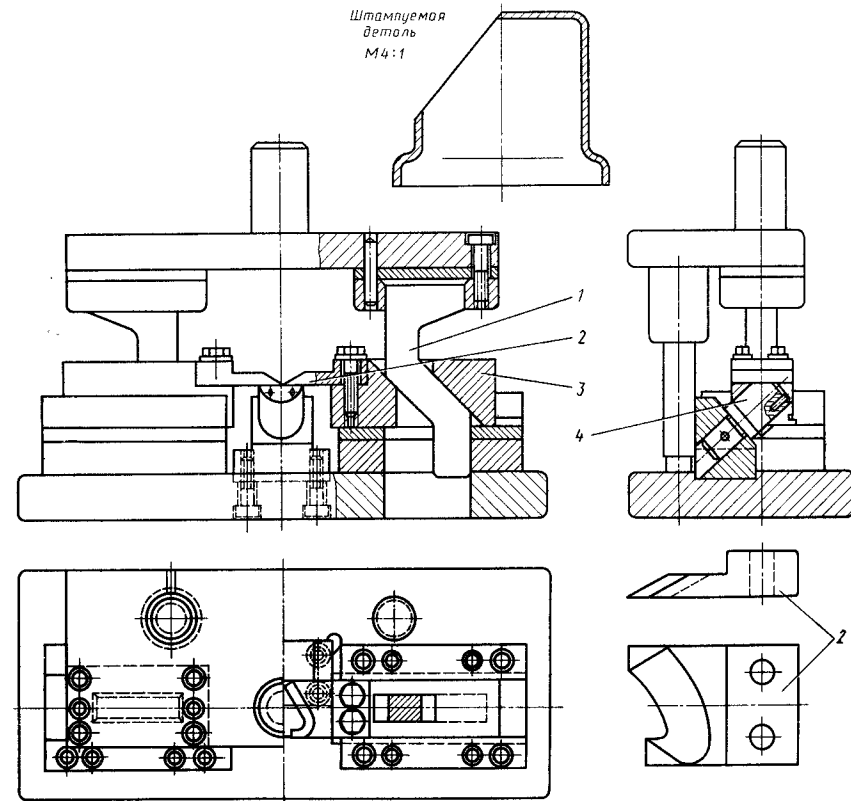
Конструкция штампа для снятия лысок на поверхности полой детали
